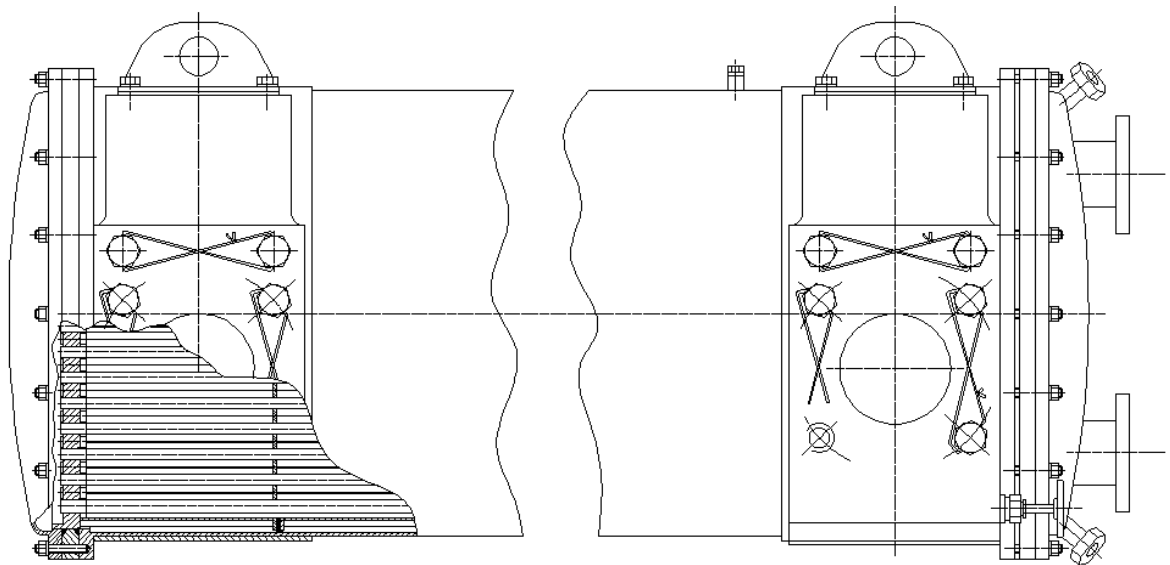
Загальний вигляд кожухотрубного МО дизеля 16 ЧН 26/26
